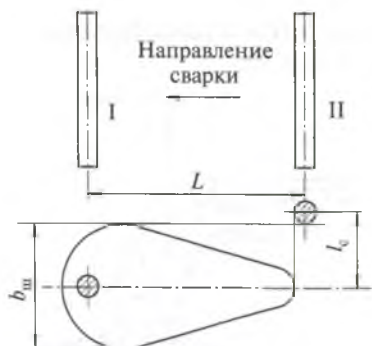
Схема двухдуговой сварки смещенными электродами
